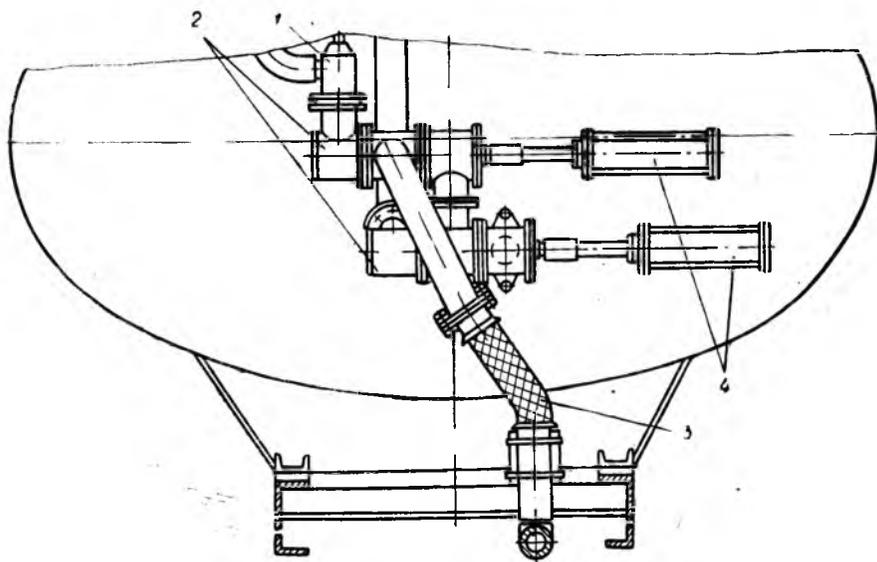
Схема включения эжектора в систему набора воды и обогрева цистерны: 1 — эжектор; 2 — газораспределители; 3 — металлорукав; 4 — пневмоцилиндры
